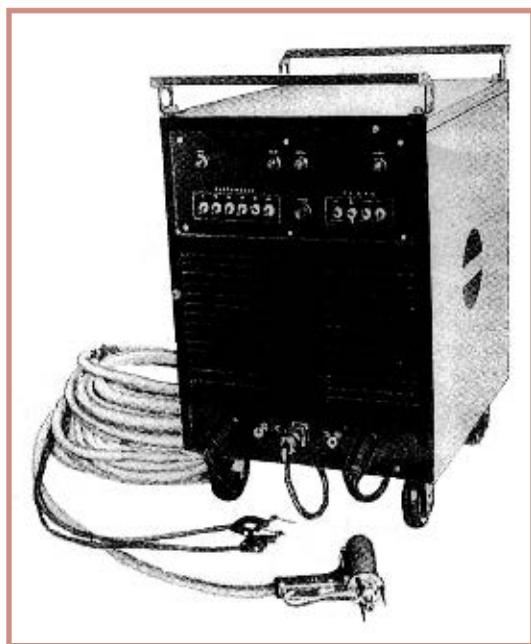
Установка К-747 МВ для конденсаторной приварки шпилек
